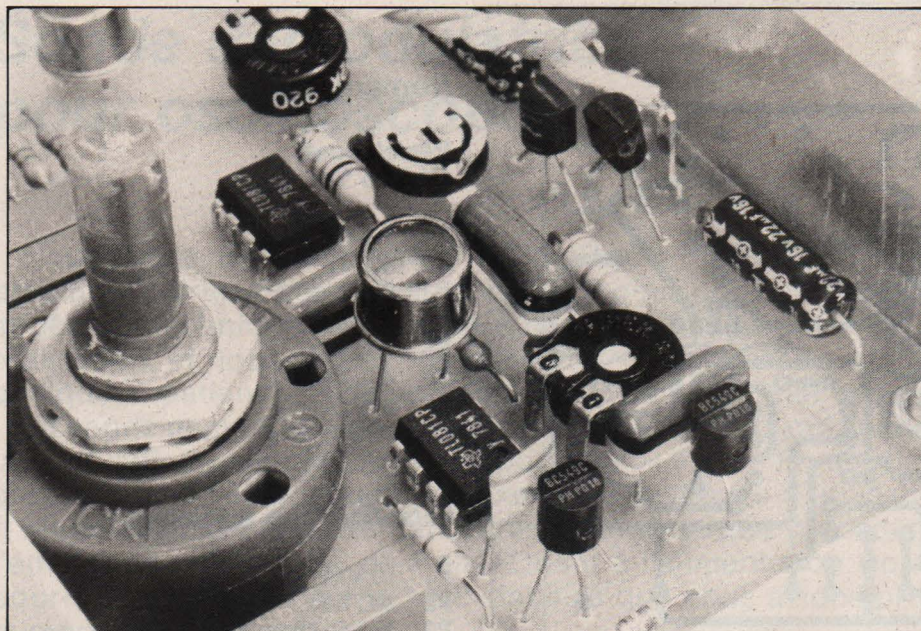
La photodiode est soudée en conservant toute la longueur des pattes.
